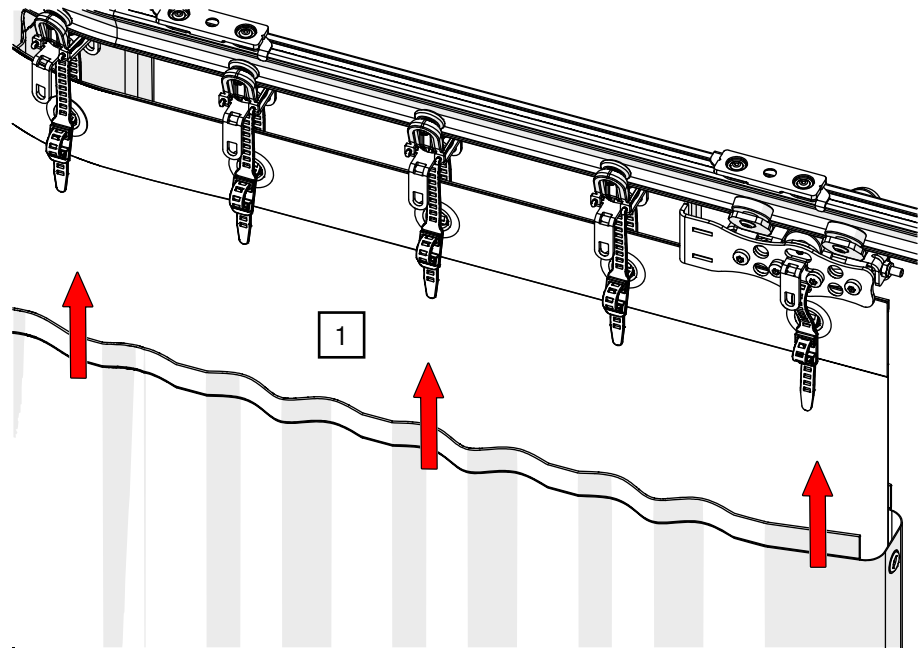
Zugwagen – Außenlagen anheben und positionieren (2/2)
